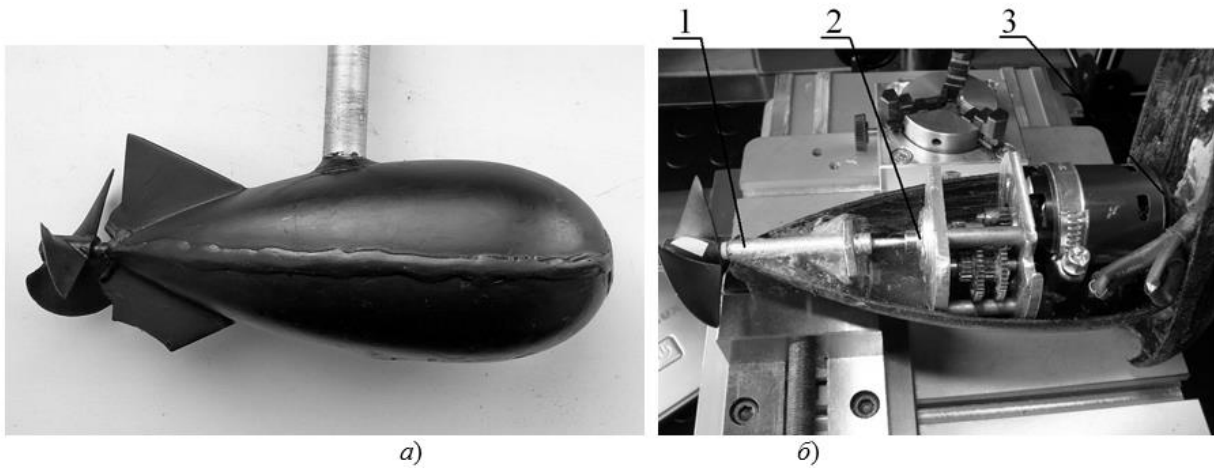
Расположение элементов в АВПК: а) – внешний вид мотогондоллы; б) – внутренняя конструкция; 1 – дейдвудный подшипник; 2 – опорный подшипник; 3 – упорный подшипник
